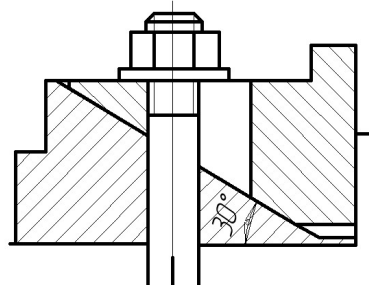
Схема клинового механізму для передавання зусилля затиску заготовки
